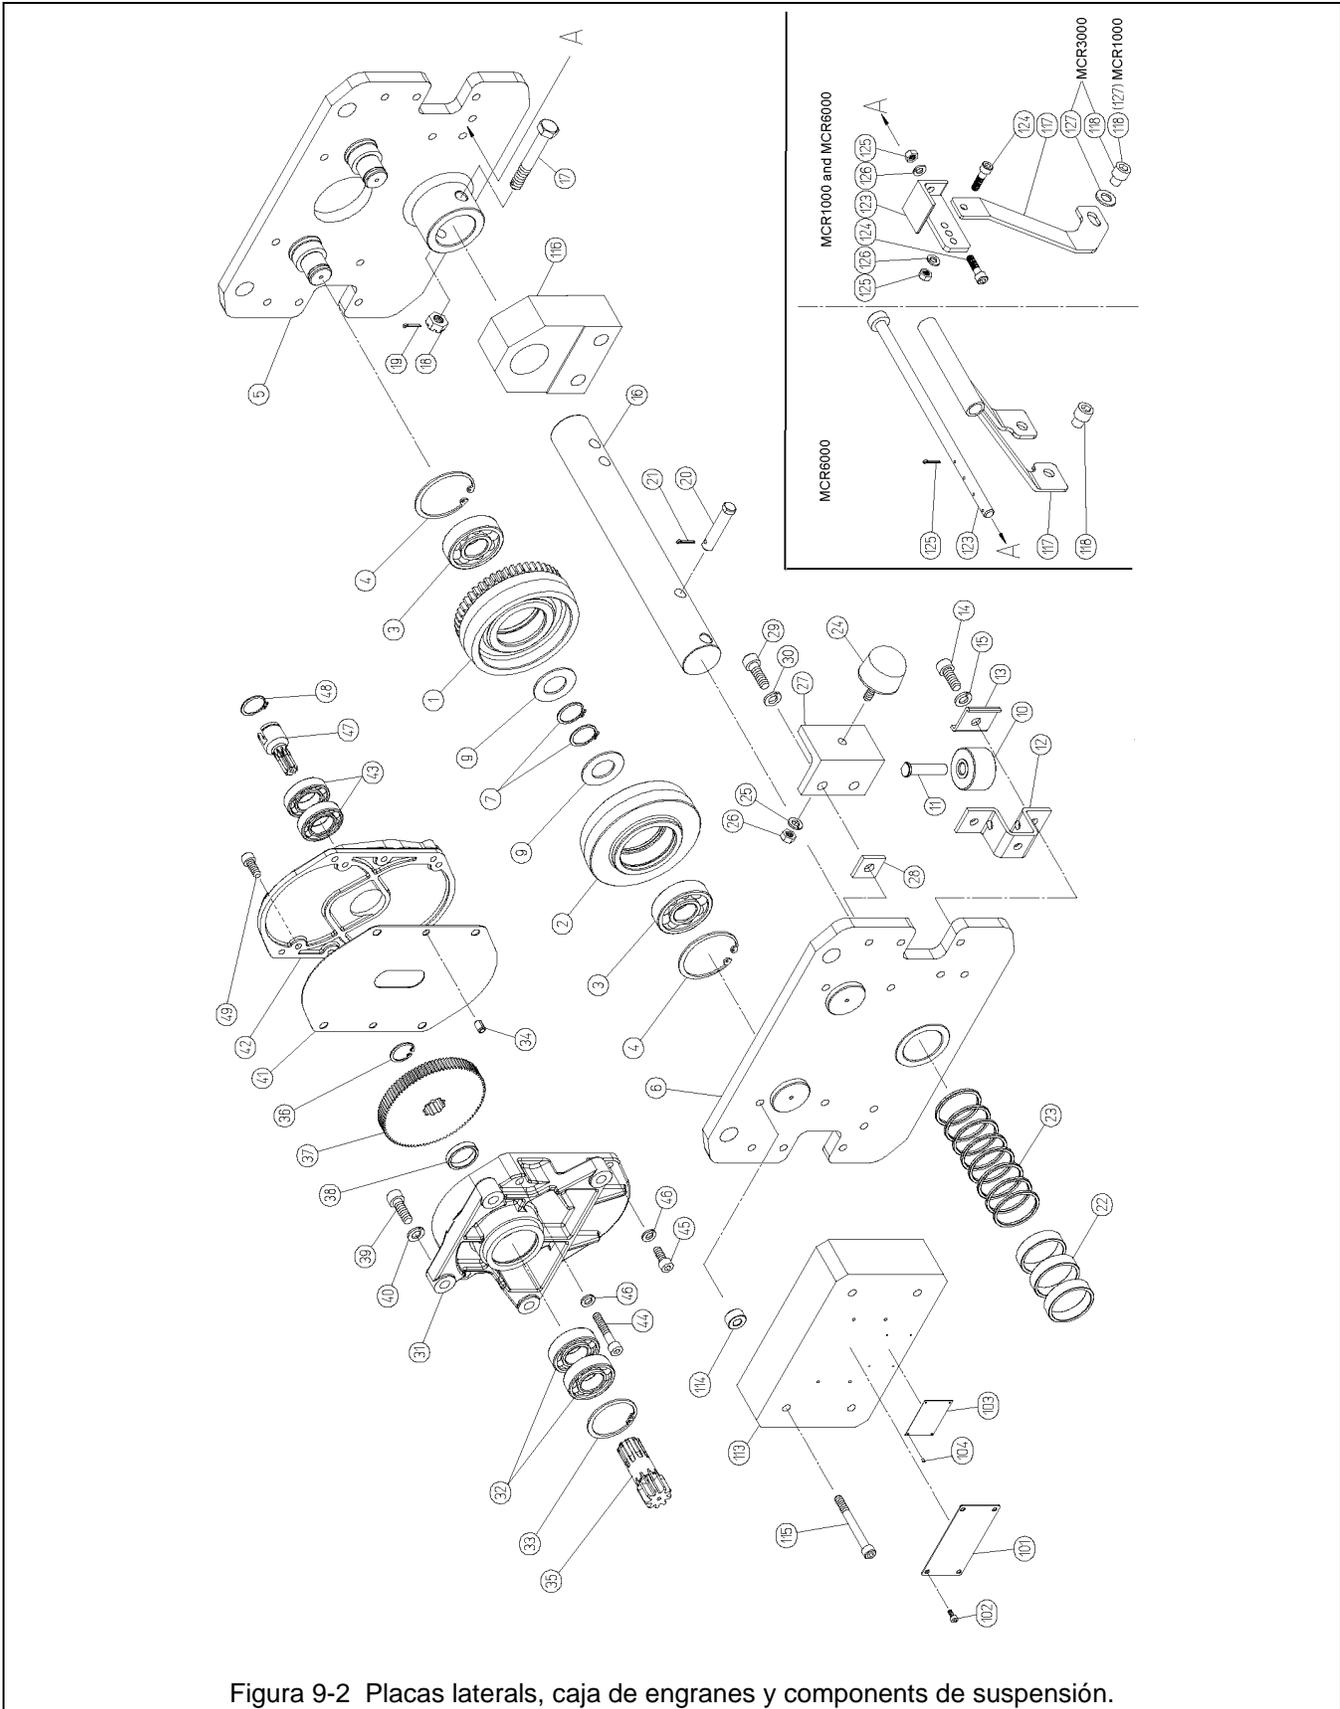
Placas laterales, caja de engranes y componentes de suspensión.
